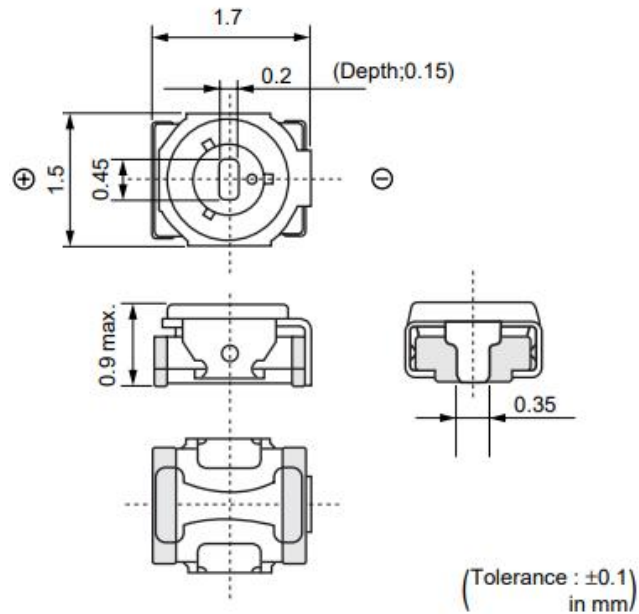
Габаритні розміри підстроювального конденсатора серії TZC3
